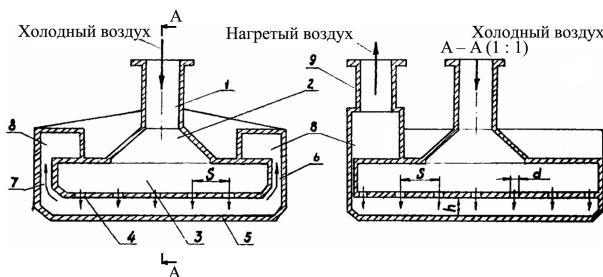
Схема модуля струйного рекуператора конструкции Института газа: 1 — подводящий патрубок; 2 — диффузор; 3 — успокоительная камера; 4 — сопла; 5 — поверхность теплообмена; 6, 7 — щели для отвода воздуха; 8 — П-образный воздухосборник; 9 — отводящий патрубок.
